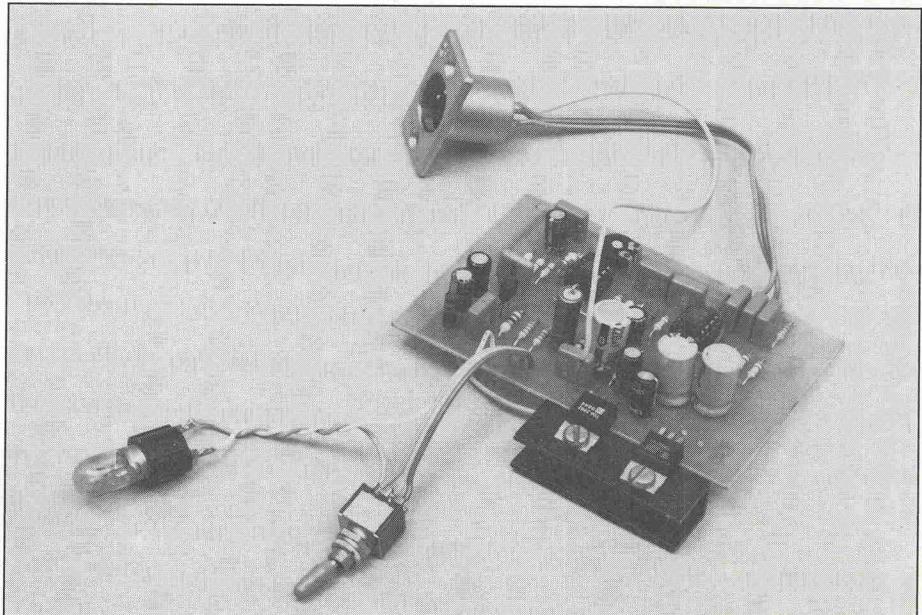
Die bestückte Intercom-Platine mit externer Beschaltung.
